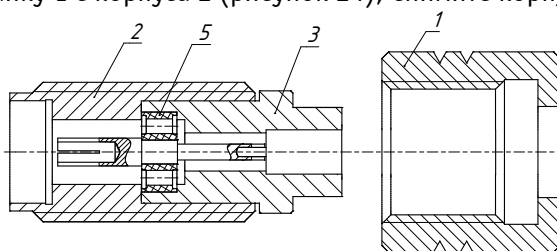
Кабельный соединитель РК1-40-14Р-2 с отсоединенной стягивающей гайкой
